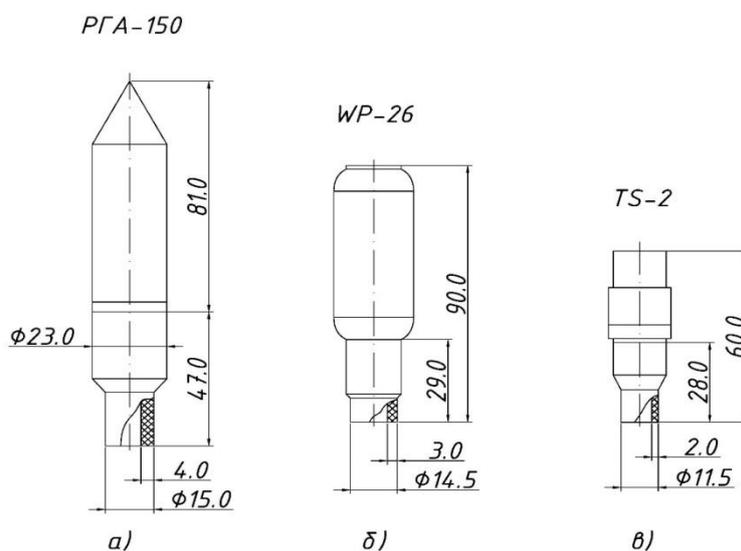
Эскизы горелок типа PGA-150(а), WP-26(б), TS-20(в) для ручной аргонодуговой сварки
